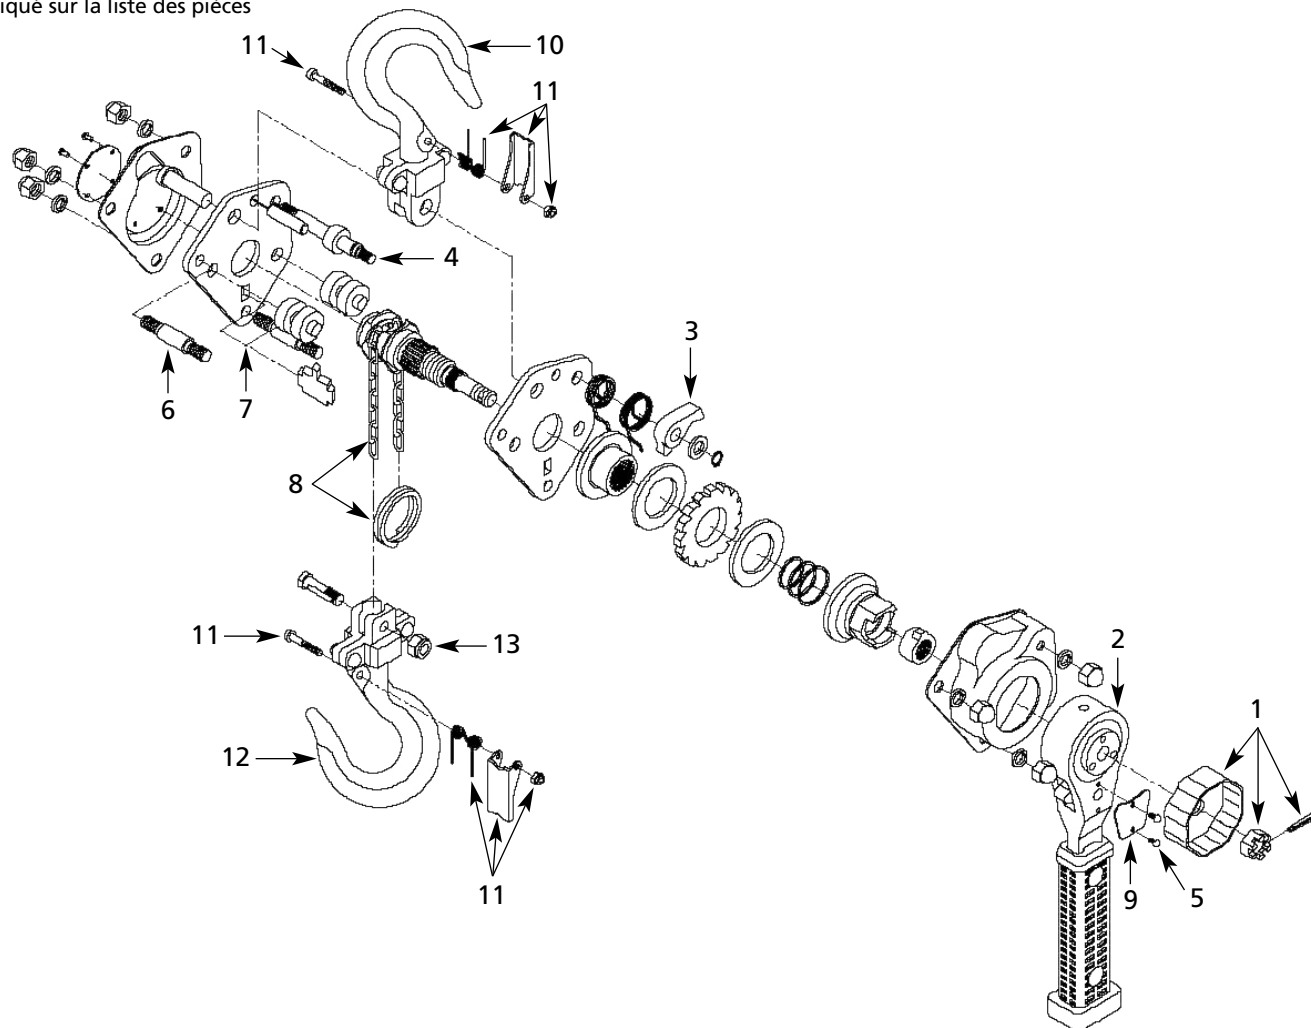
Illustration des pièces détachées pour le palan à chaîne à levier
